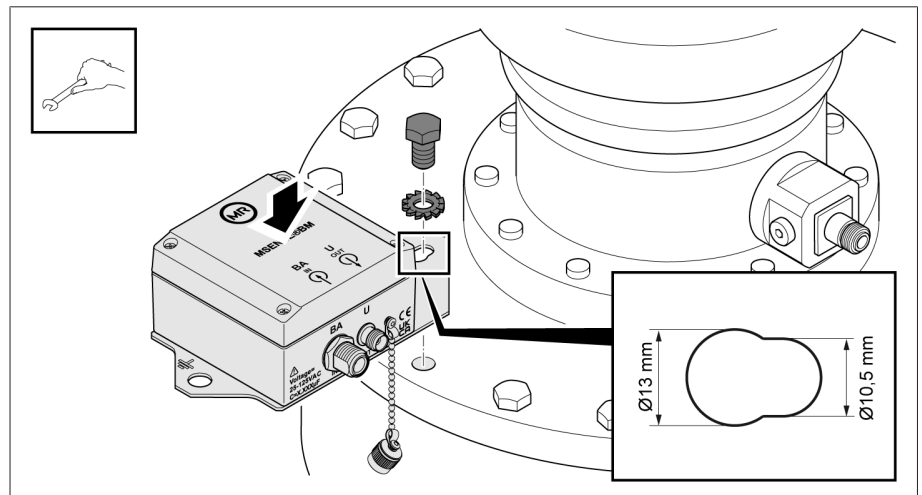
Montaje de la chapa de sujeción en la brida para aislador pasante
